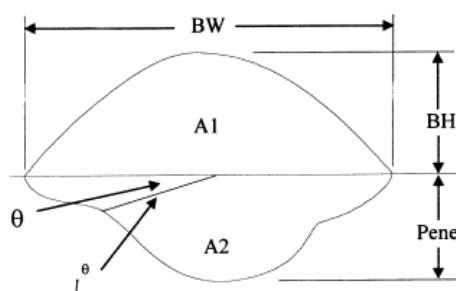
Parâmetros geométricos do cordão de solda.
